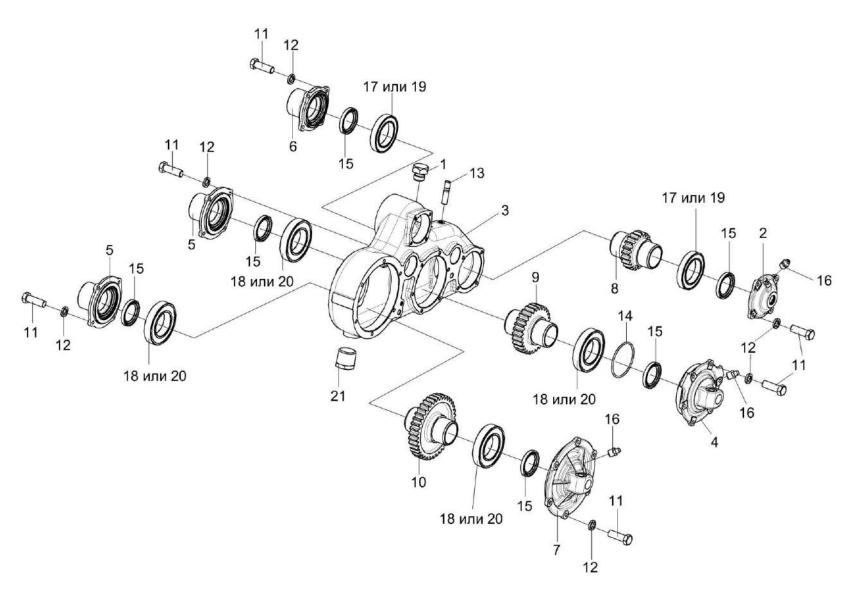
Редуктор верхних вальцев КВК 0112100 (лист 1)
